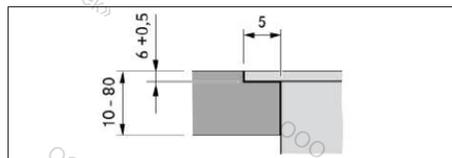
Размеры опорной конструкции для накладного монтажа
